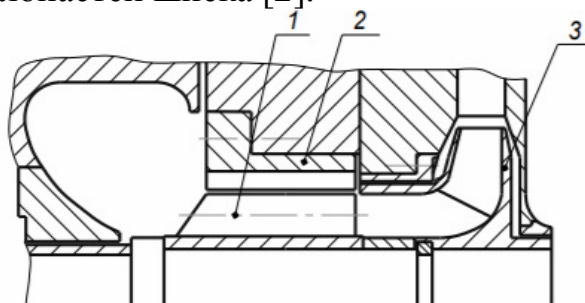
Схема осевихревой ступени: 1 – осевое колесо (шнек); 2 – неподвижная втулка с лопатками; 3 – центробежное колесо
